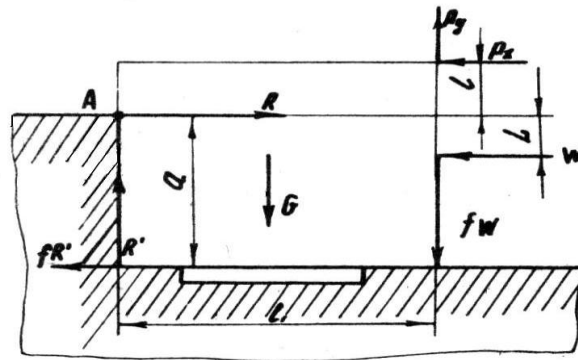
Схема розрахунку затискних зусиль при обробці заготовки на фрезерному верстаті в пристосуванні лещатного типу.
